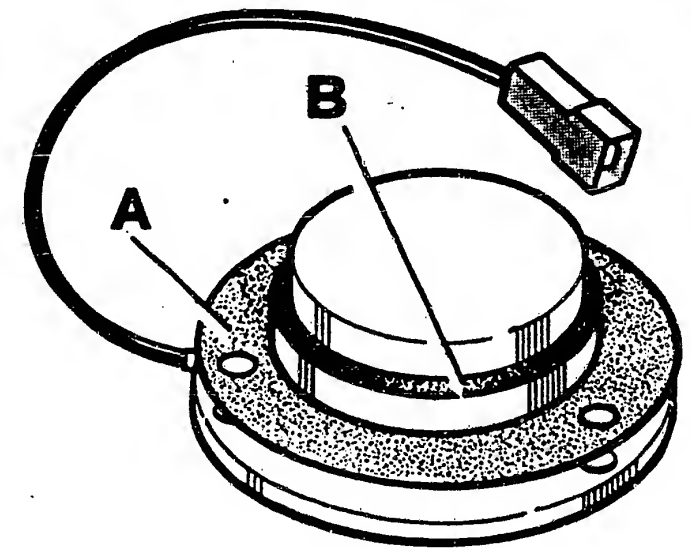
Die Heizplatte im Ansaugkrümmer der Vergasermotoren ist mit einer Papierdichtung (A) und einem O-Ring (B) abgedichtet.
